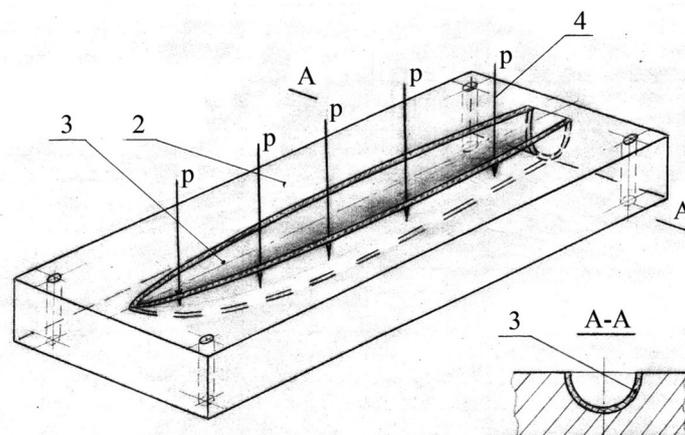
Процесс формирования изделия в нижней половине матрицы после нагрева заготовки
